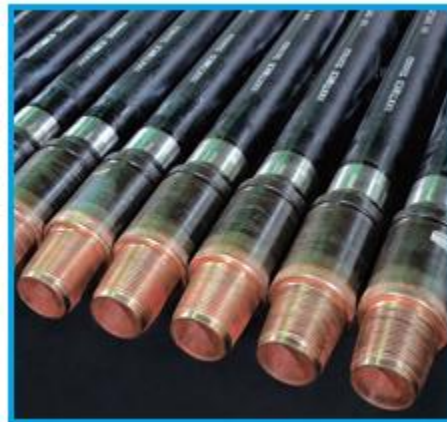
Drill rods usados para la perforación del suelo en busca de agua, soldados en sus extremos por fricción.
